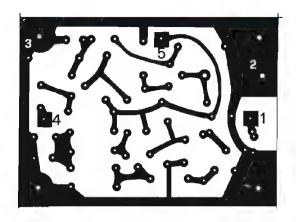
Disegno del circuito stampato sul quale si realizza il cablaggio del convertitore. Si tenga presente che questo disegno è in scala unitaria.
